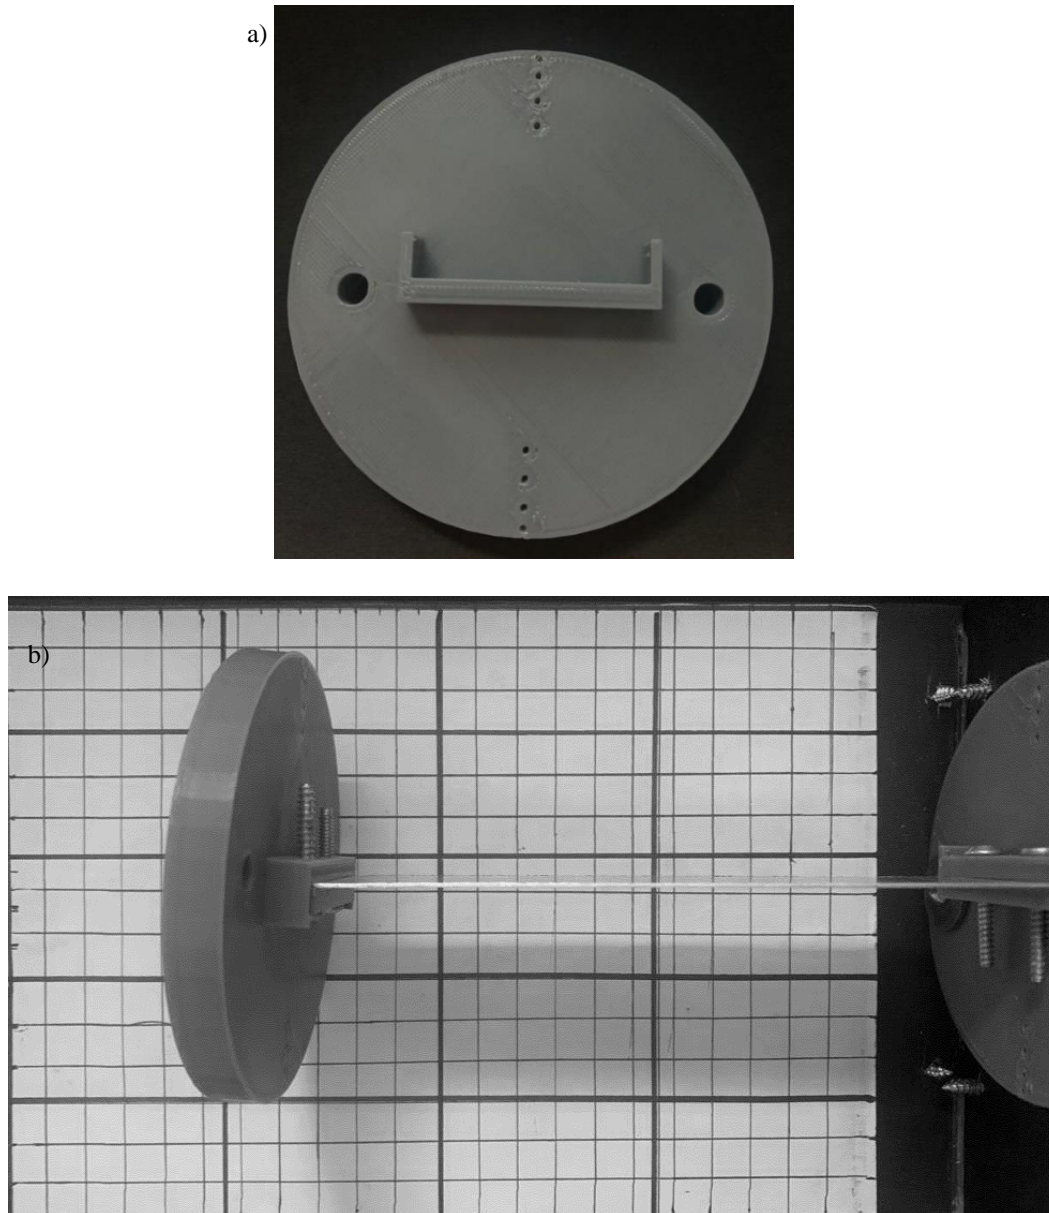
20: Fabricación y ensamblaje de componentes de un manipulador flexible, a) disco lateral fabricado por PLA y b) manipulador sin alambre de SMA.
